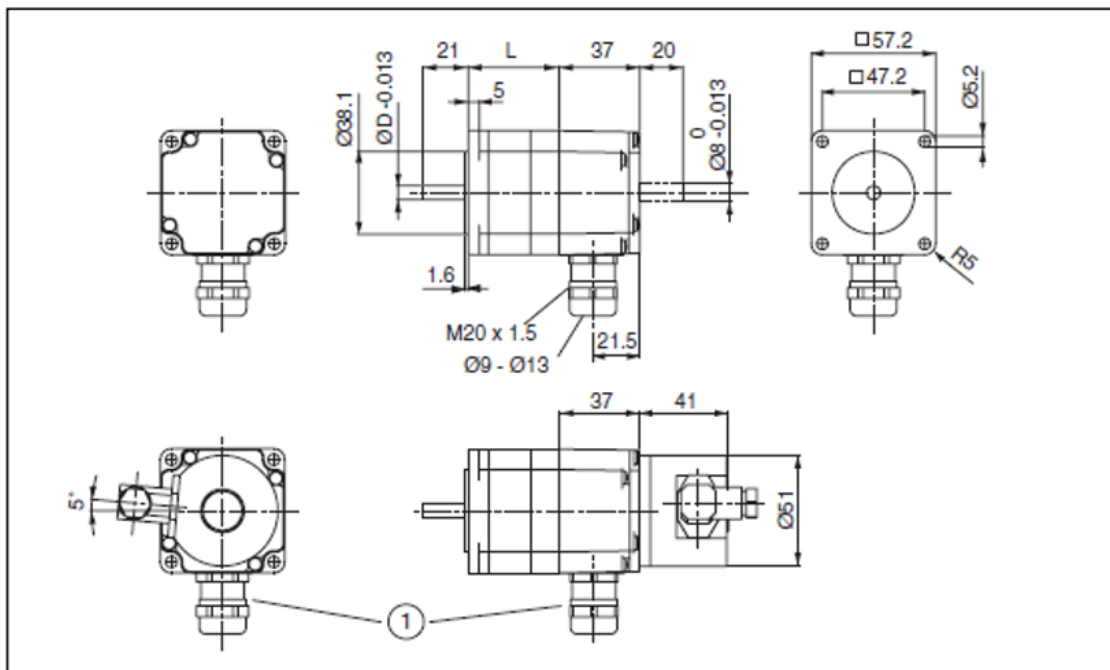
Schema motorului pas cu pas BRS36 [5]
